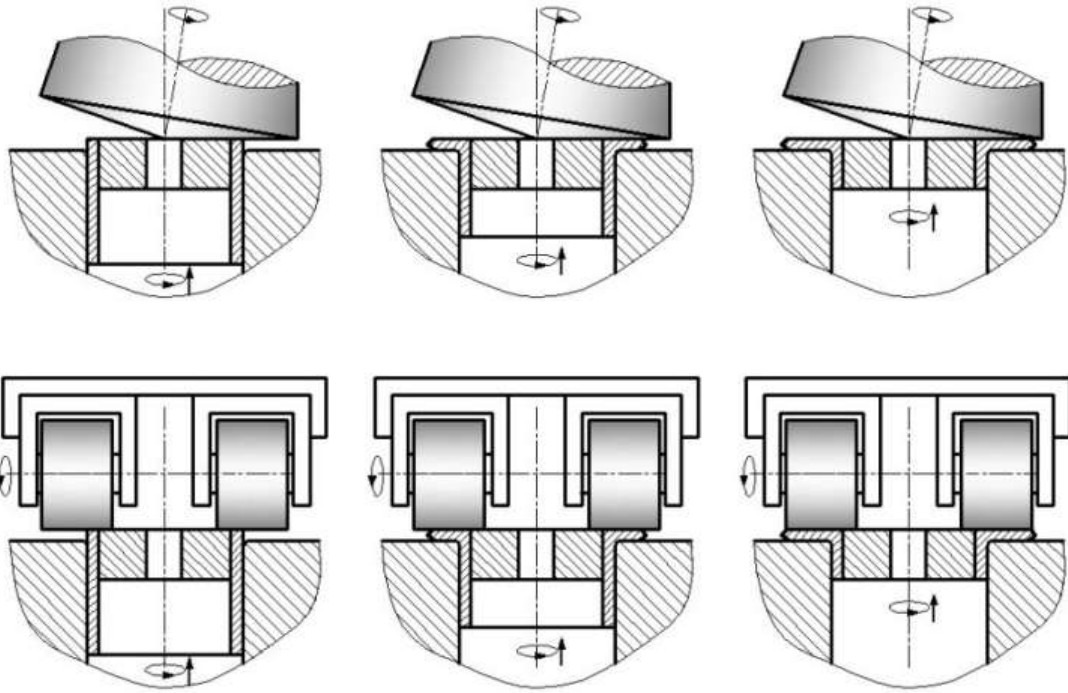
Схеми комбінованої торцевої розкатки кільцевих деталей конічними і циліндричними валками
